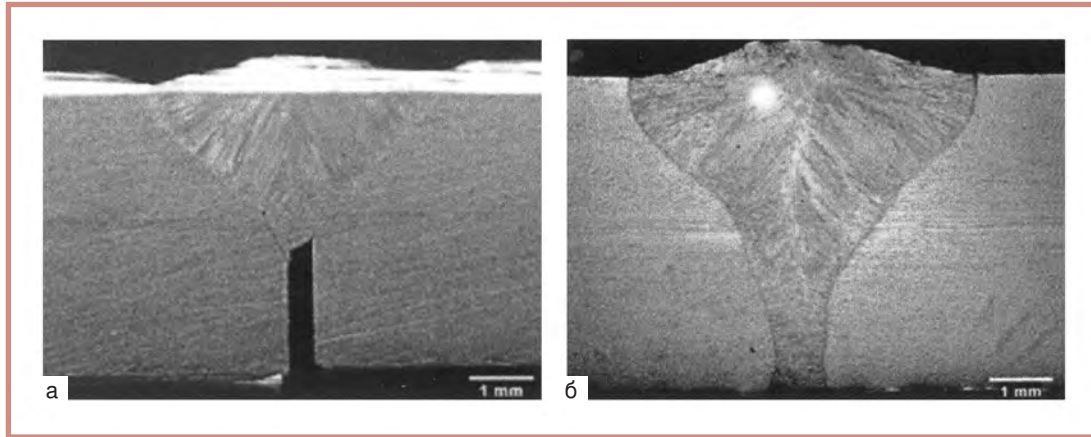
Макроструктура стыкового сварного соединения стали 172246 ($t=5$ мм, Y-образная разделка кромок), выполненного гибридной сваркой лазер+ MAG (а) и MAG сваркой (б) с величиной зазора 0,5 мм
